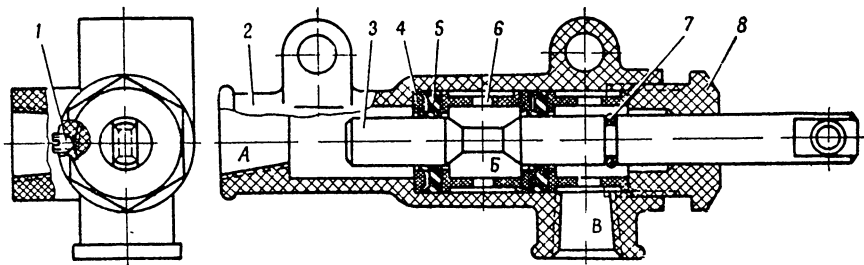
Конструктивная схема крана управления давлением золотникового типа
